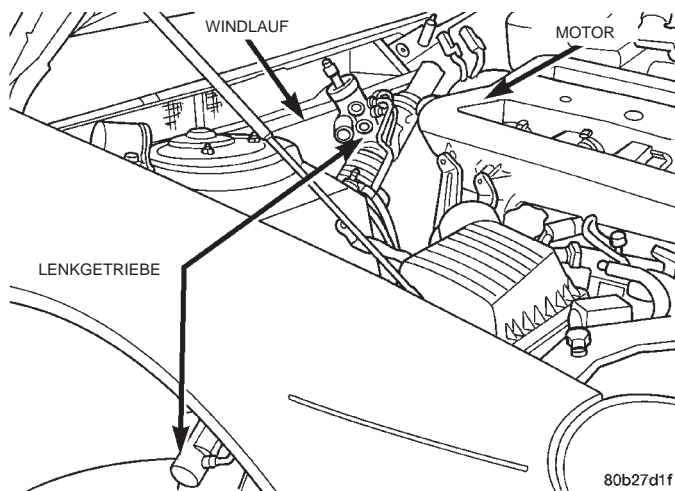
Schräglage des Lenkgetriebes zum Ausbau
